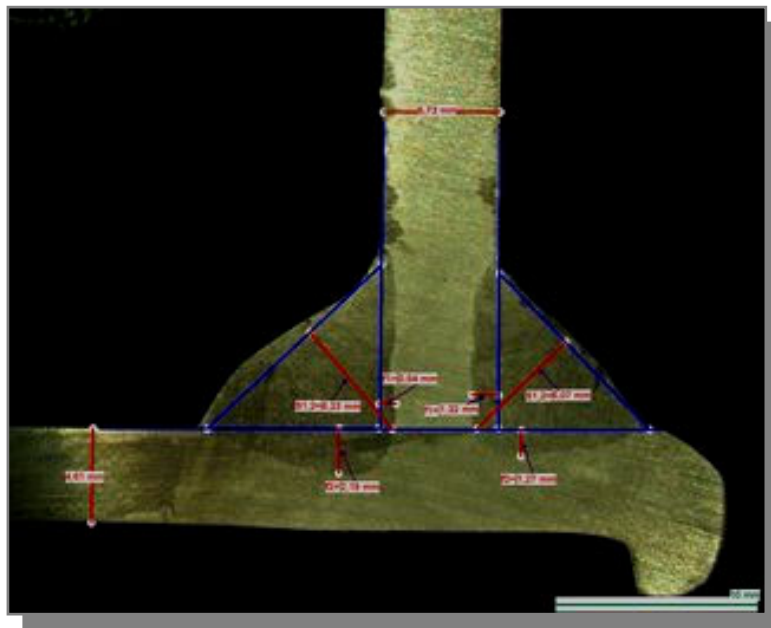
Beispiel einer Schweißnahtvermessung
